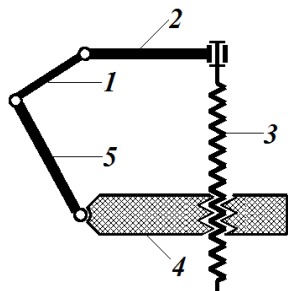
Шестизвенный механизм с неподвижным звеном 4
